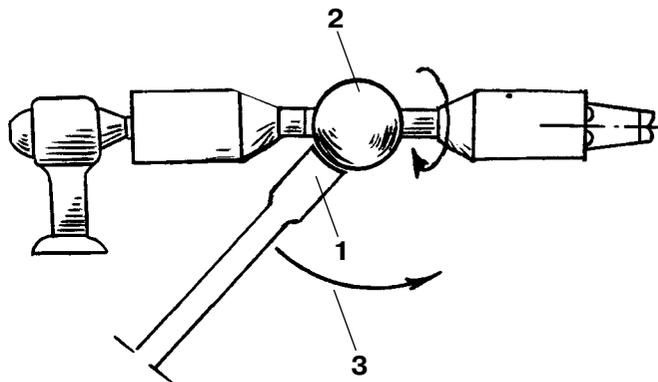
Точение шара: 1 — лезвие стамески; 2 — заготовка; 3 — движение стамески.
